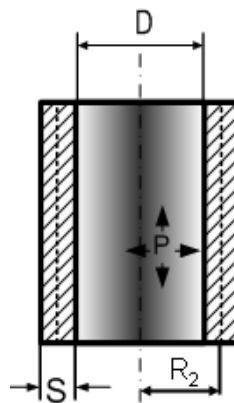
Схема к расчету цилиндрического корпуса
